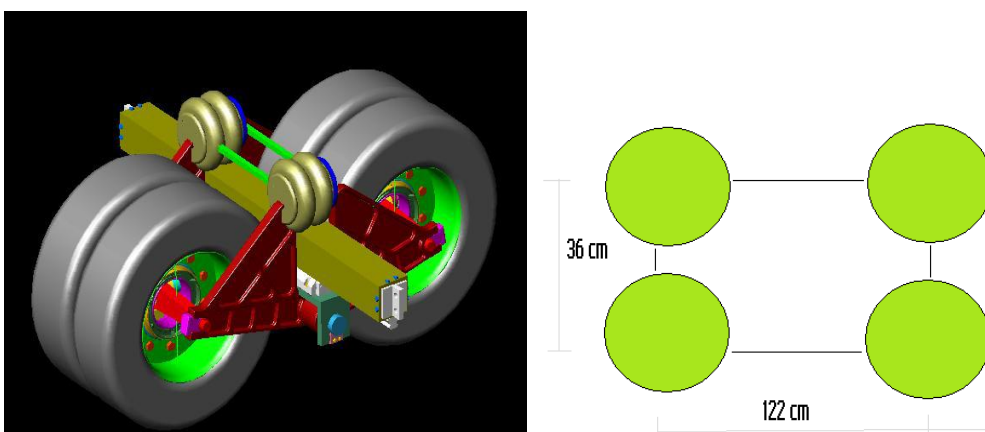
b.34 Eje Tandem W = 18 Ton.
